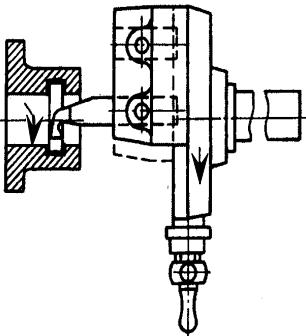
Рухомий супорт для проточування внутрішньої канавки
